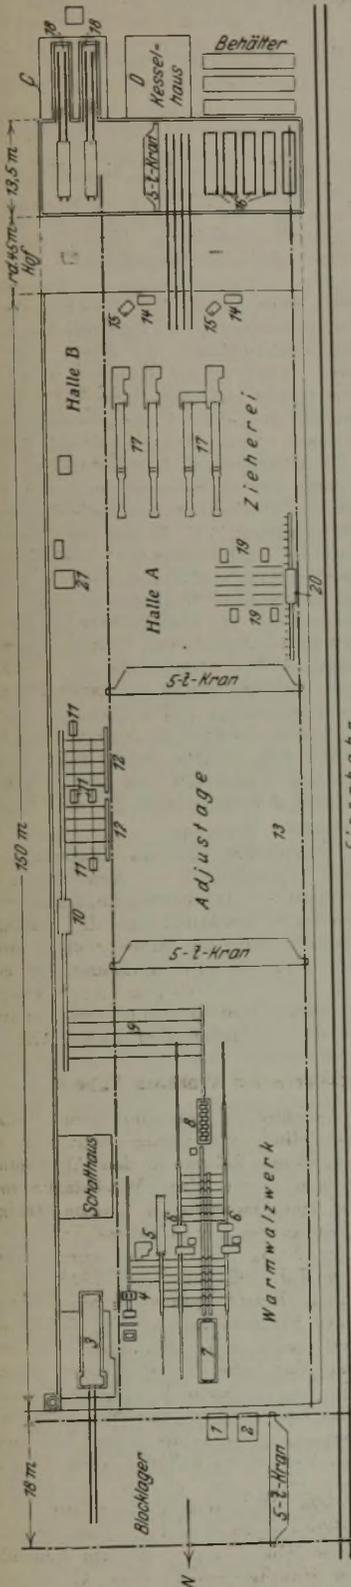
Lageplan des Rohrwalzwerks der Weldless Tube Co.
